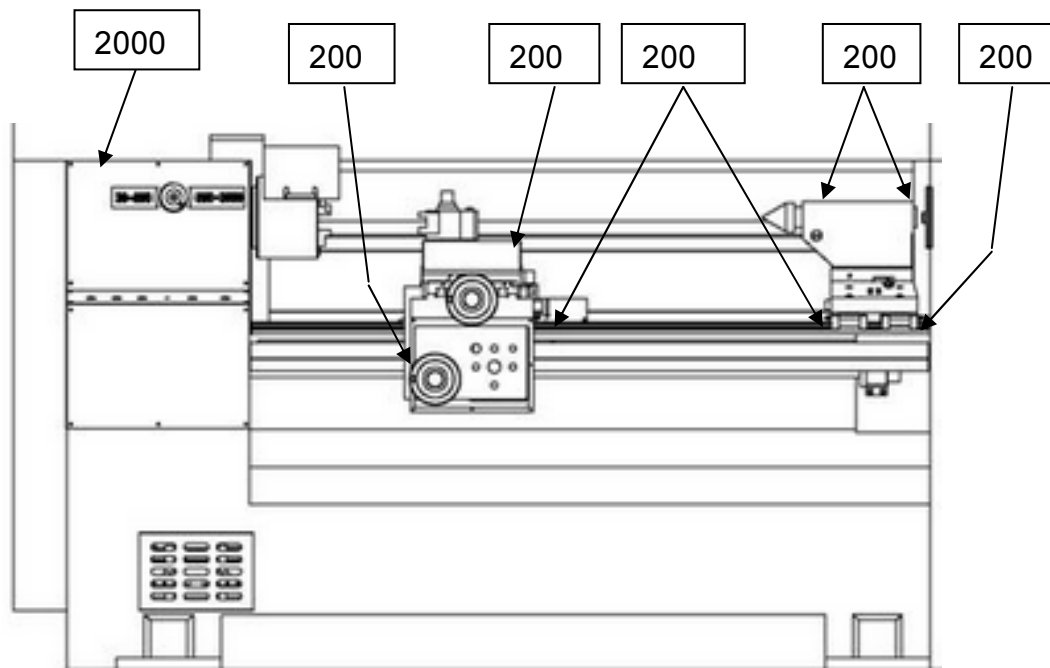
Schmierplan mit Betriebsstunden (Abbildung ähnlich)
